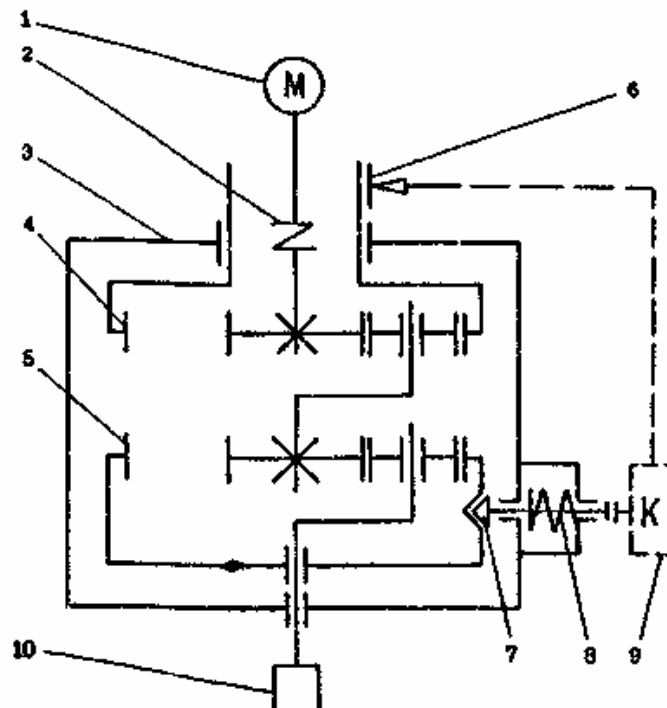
Схема электромеханического гайковерта: 1 – электродвигатель; 2 – муфта; 3 – корпус; 4 и 5 – колеса корончатые; 6 – тормоз колодочный; 7 – конический стержень; 8 – пружина; 9 – конечный выключатель; 10 – шпиндель
